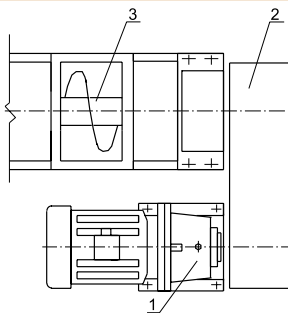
Привод винтового конвейера на базе планетарного мотор-редуктора (с клиноременной передачей):
